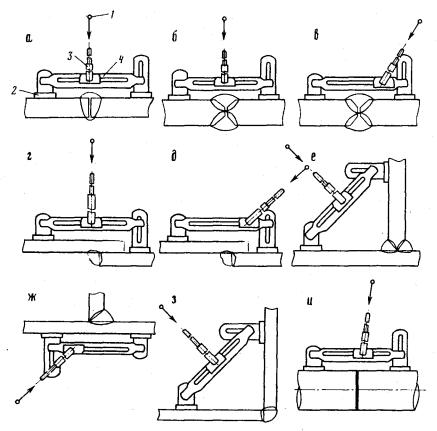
Схемы расположения центратора при просвечивании сварных соединений различных типов:
